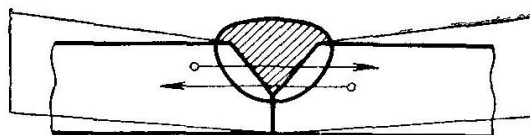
Угловая деформация при сварке стыкового соединения
